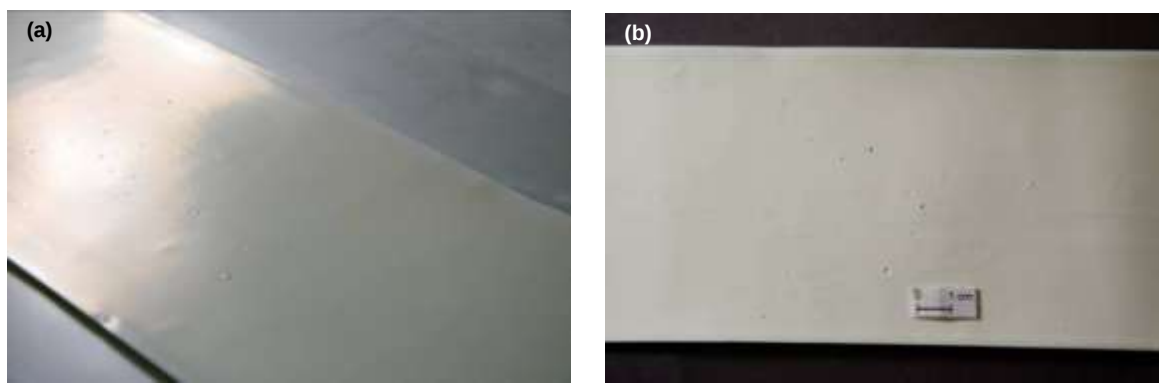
Imagens das fitas produzidas por *tape casting* após secagem dos solventes: a) Form-3; b) Form-4.
